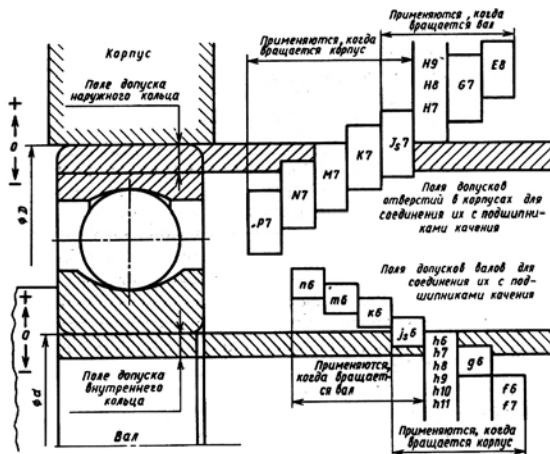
Схема расположения полей допусков на внутренний и внешний диаметры подшипников качения (на вал и в корпусе)
